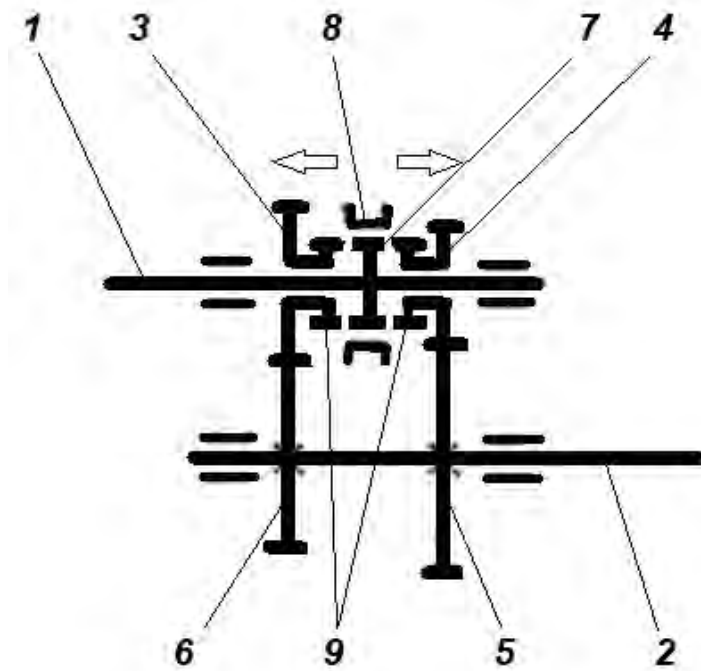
Принципова схема конструктивної реалізації коробки передач з шестернями постійного зачеплення і зубчастою муфтою [40]:
